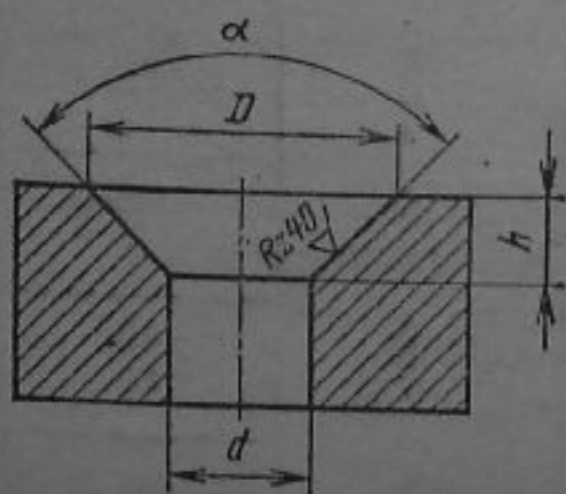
Эскиз обрабатываемой поверхности заготовки к задаче 48
